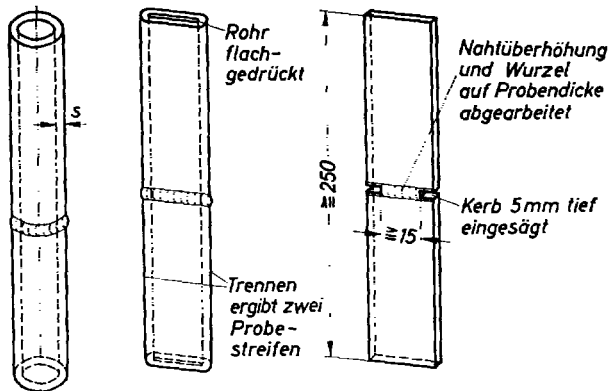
Rohr-Kerbfaltprobe F_K für Rohrschweißer an $s = 1,5$ bis 2 mm
